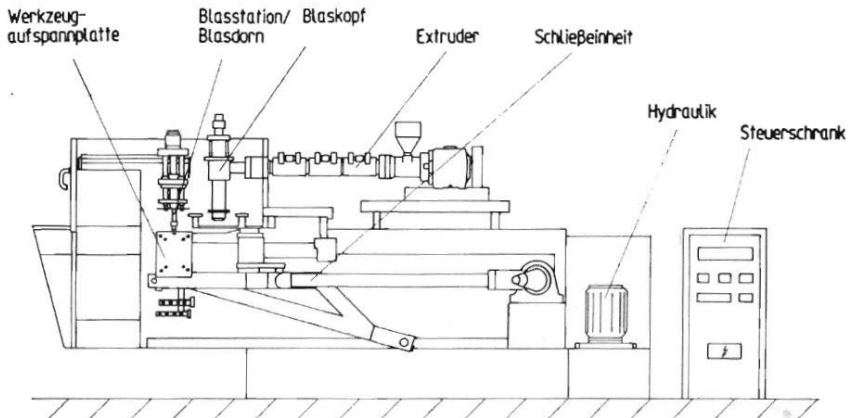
Aufbau einer Maschine für das Extrusionsblasformen [39]
